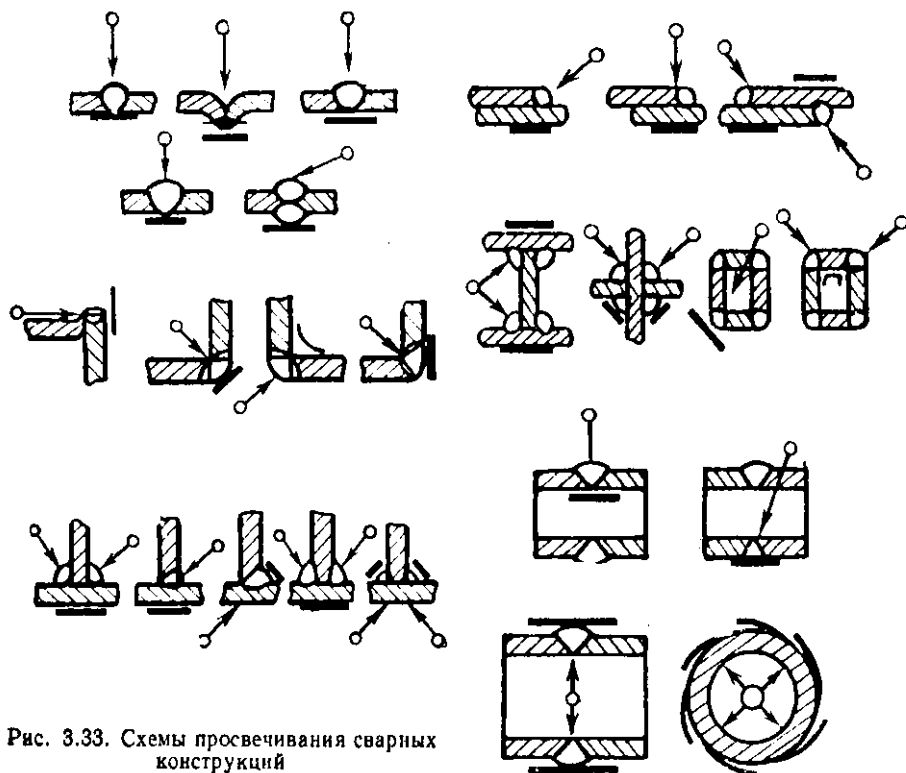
Схемы просвечивания сварных конструкций
